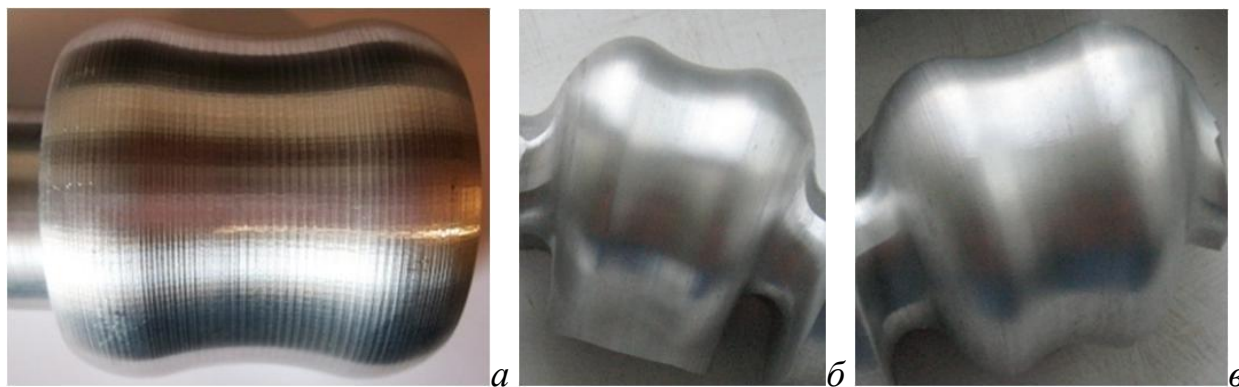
Оброблені фрезеруванням робочі поверхні протезів: сферичною (а) і циліндричною (б, в) фрезою
